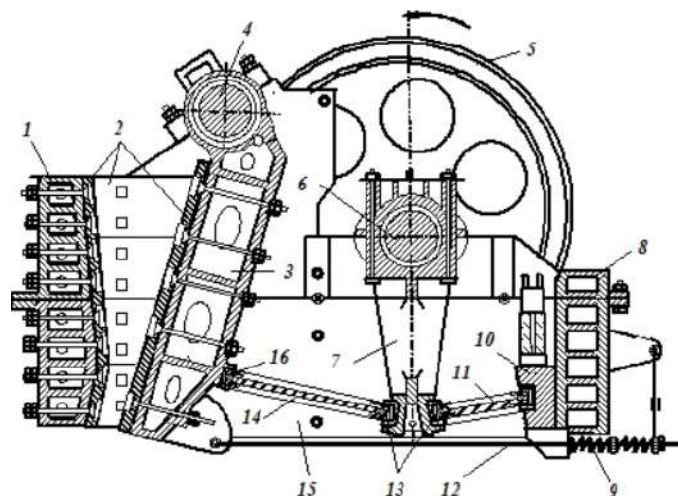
Щокова дробарка з простим рухом щоки типу ЩДП:
